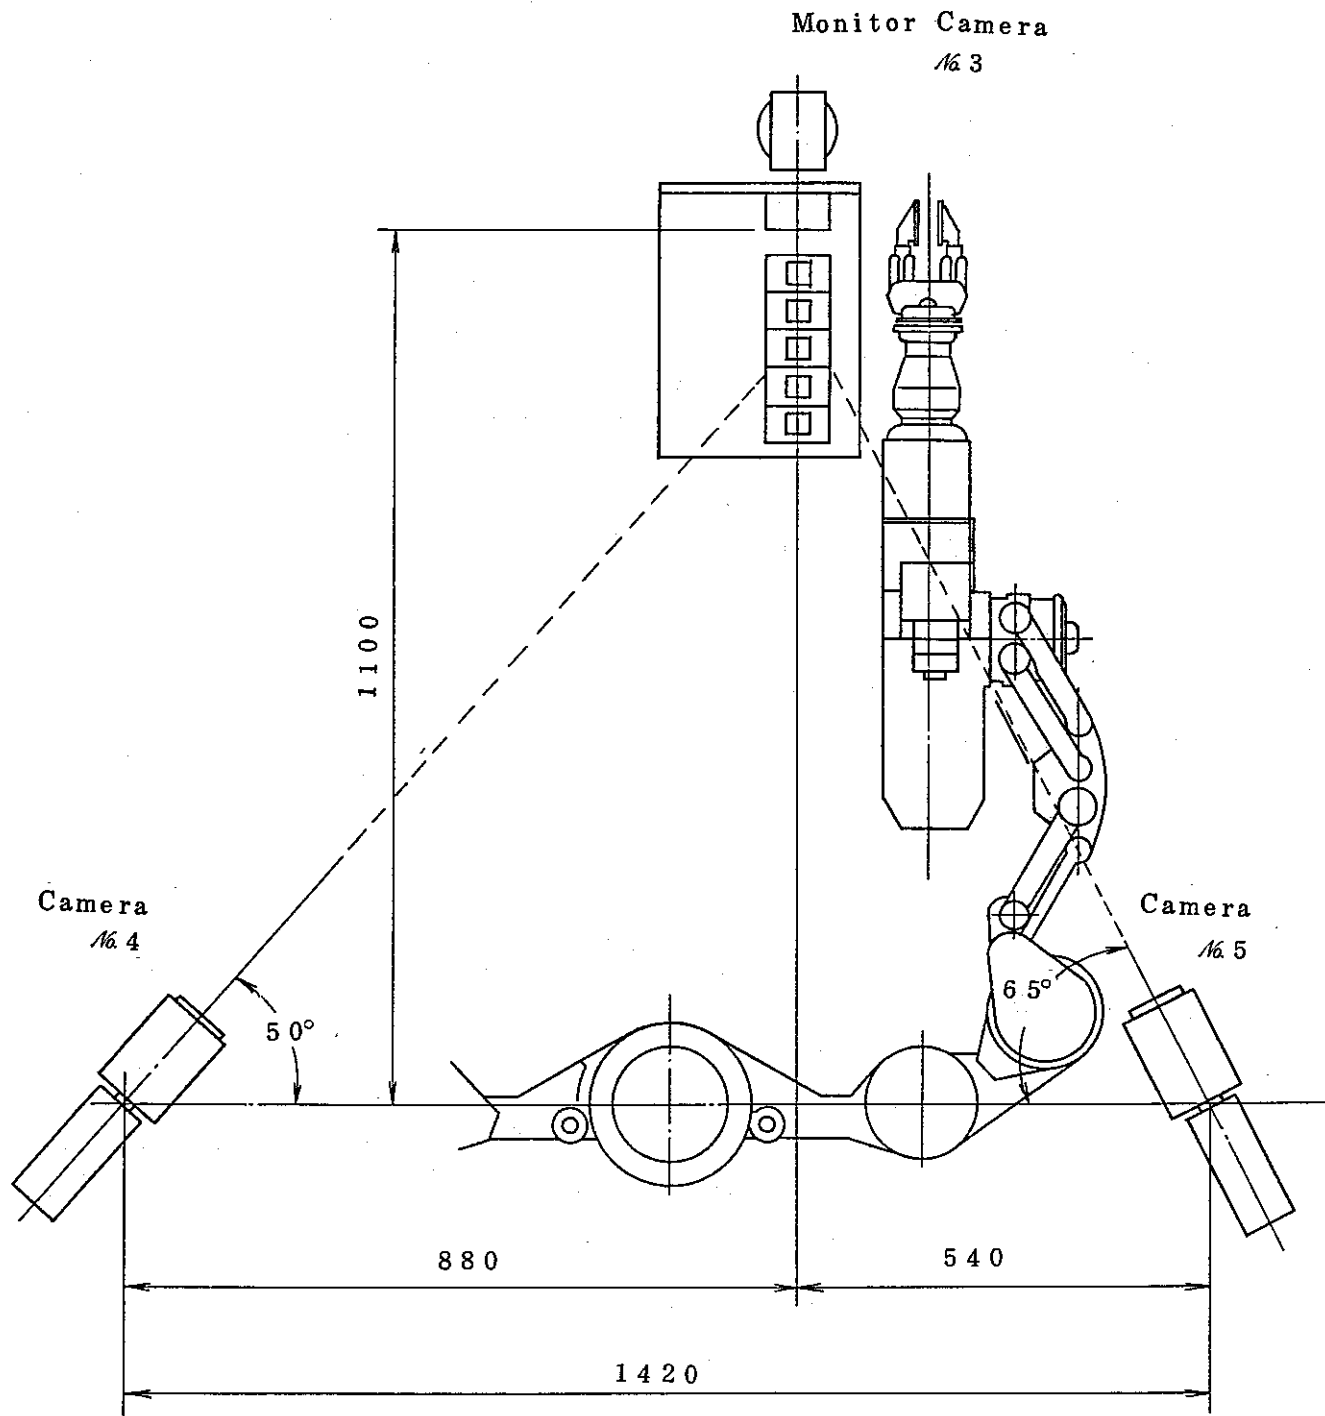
1 (1) 機器配置図 (ペグテスト平面)
